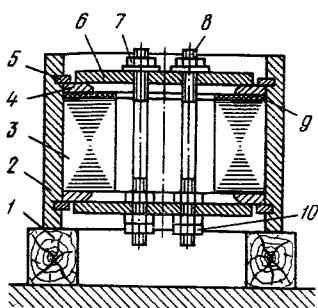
Ремонт сердечника статора с ослабленной прессовкой:
